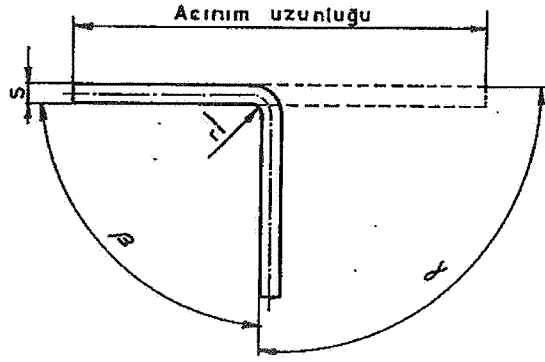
C10....C20 kalitesindeki malzemeler için,
